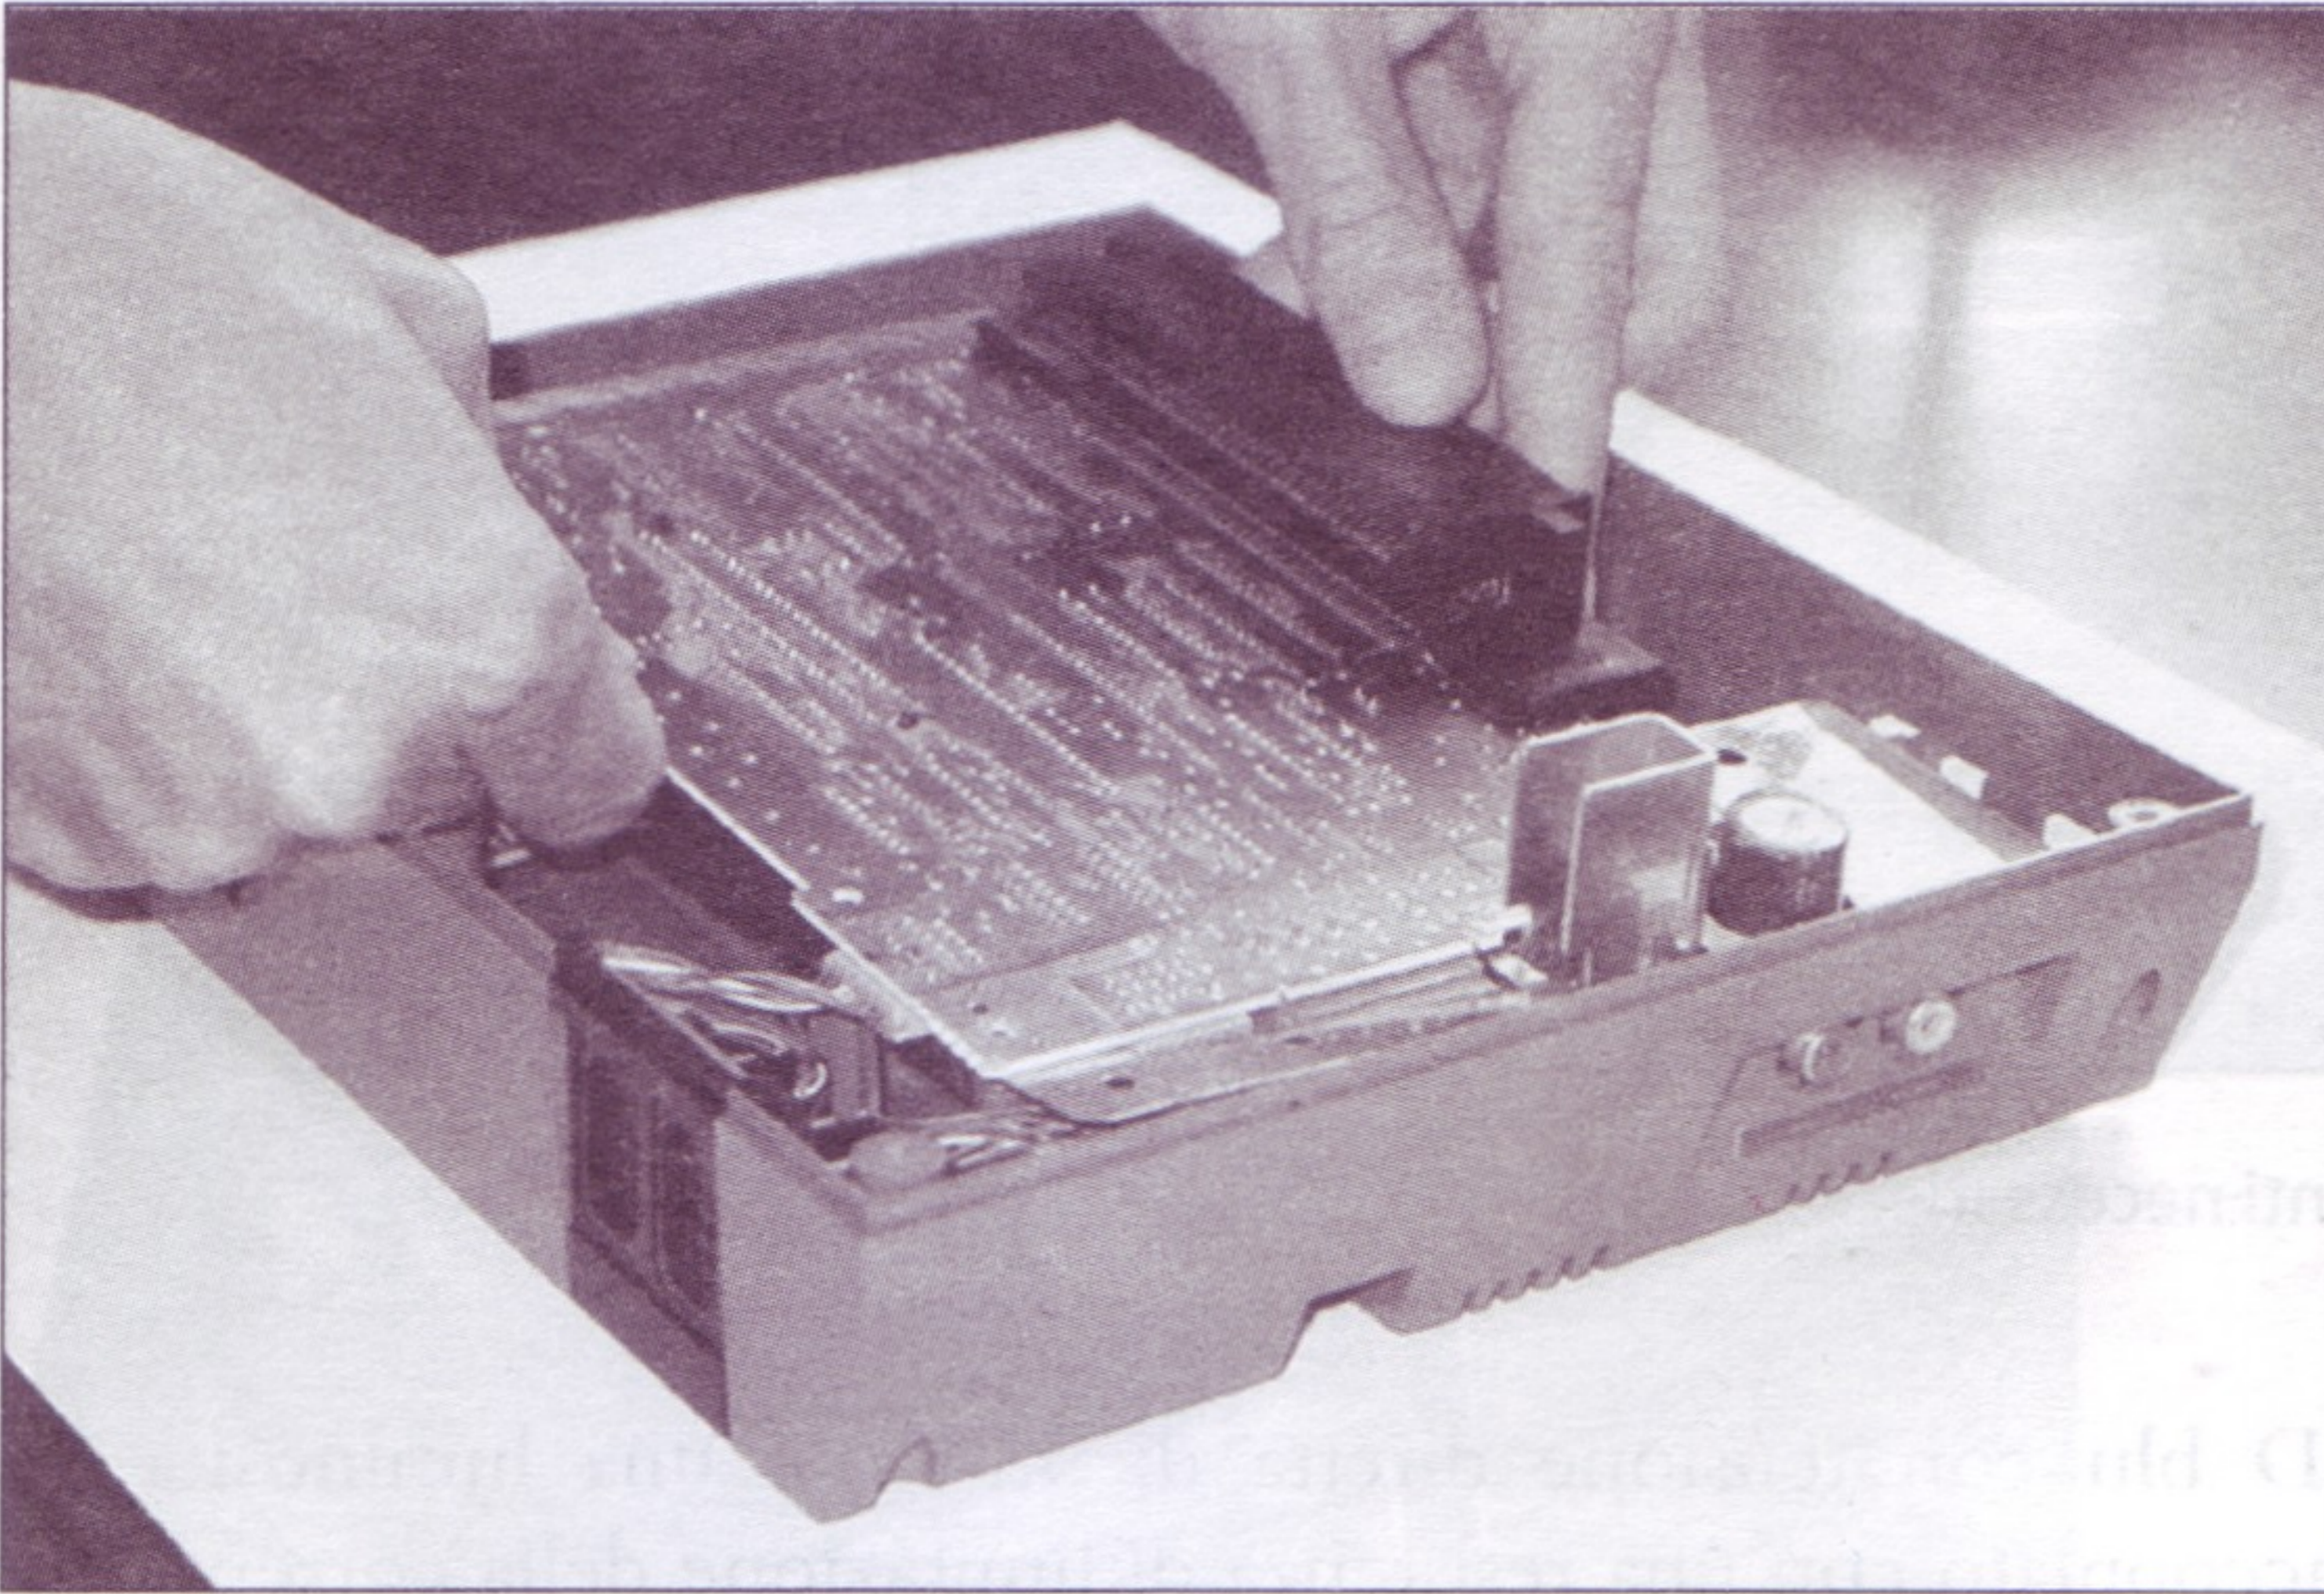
Rimozione del vecchio connettore per cartucce a 72 pin.
